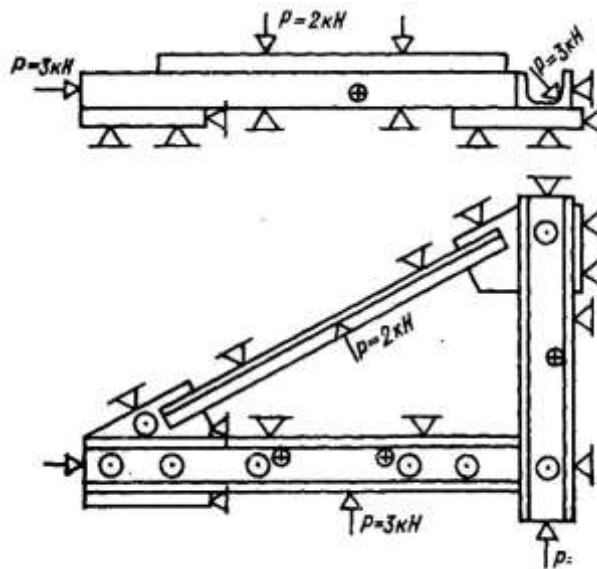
Принципиальная схема приспособления для сборки кронштейна
